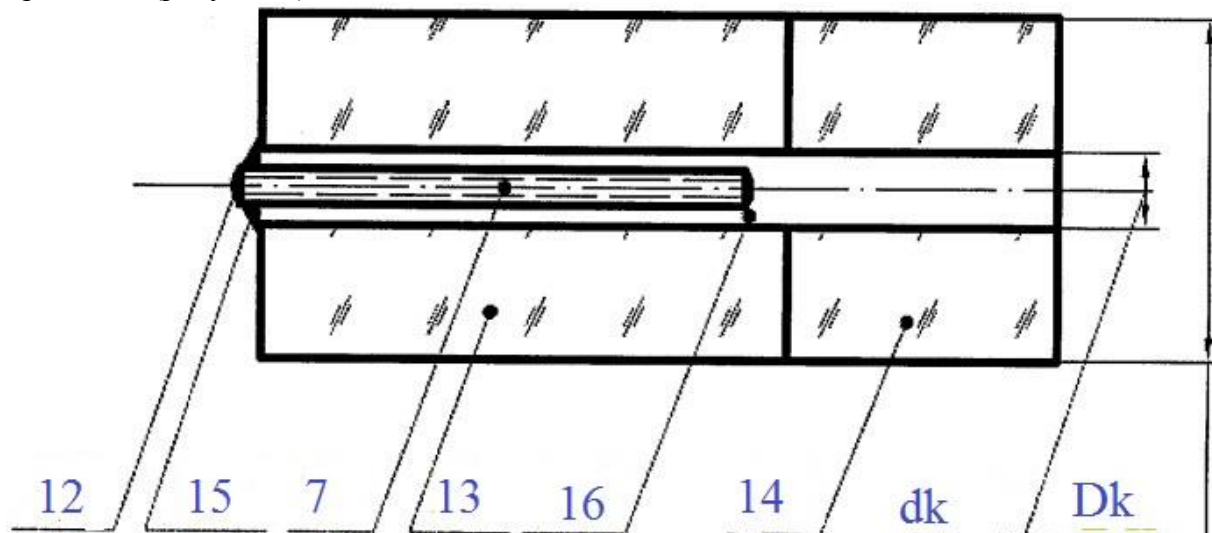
Схема сплавления предзаготовки с капиллярной трубкой
